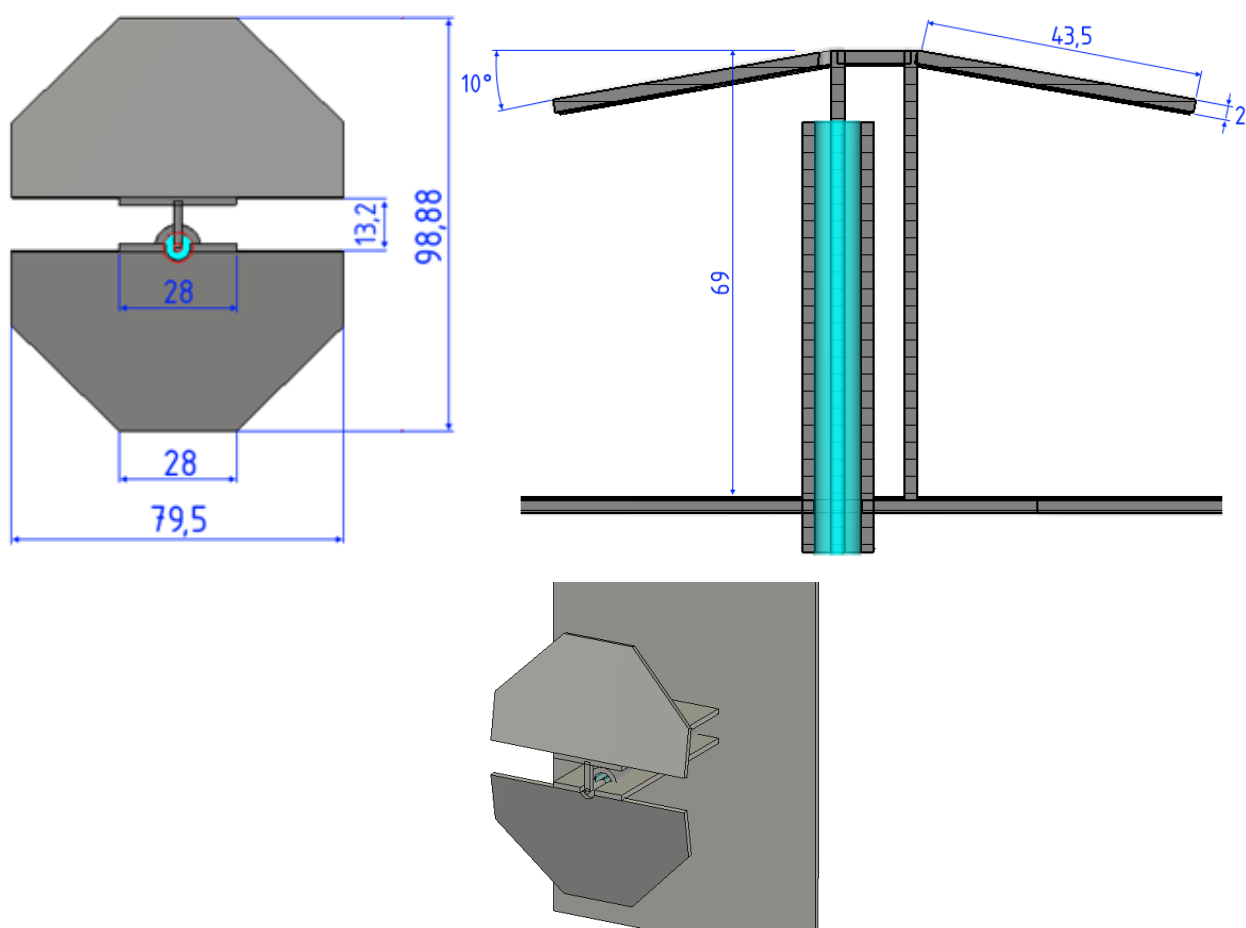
Модифицированный широкополосный пластинчатый уголкового вибраторный излучатель
